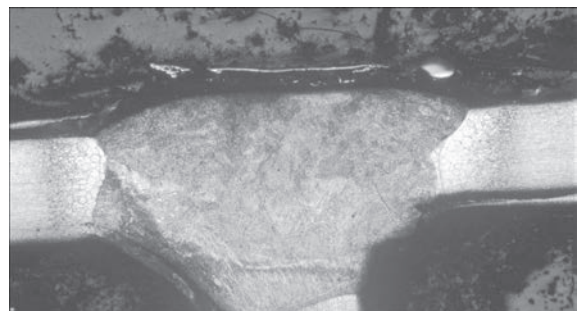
Загальний вигляд таврового зварного з'єднання після ремонтного зварювання ($\times 25$)
